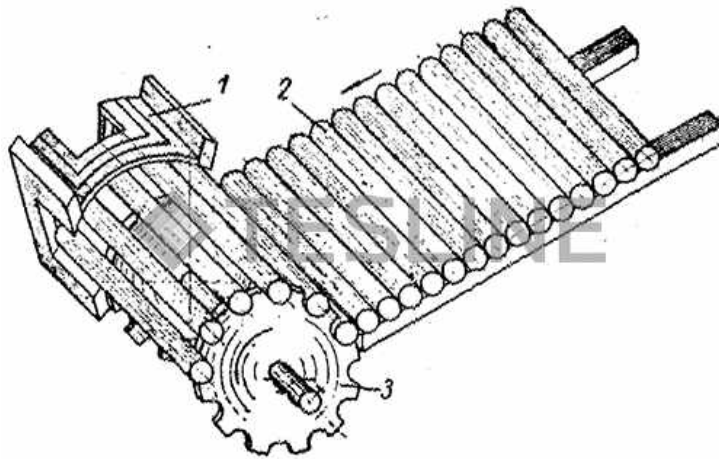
Схема нагревателя концов заготовок со щелевым индуктором:
